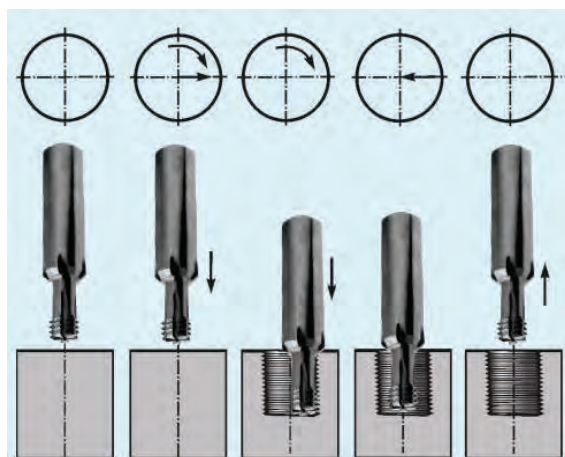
Конструкции фрезы для фрезерование резьбы в сплошном материале
